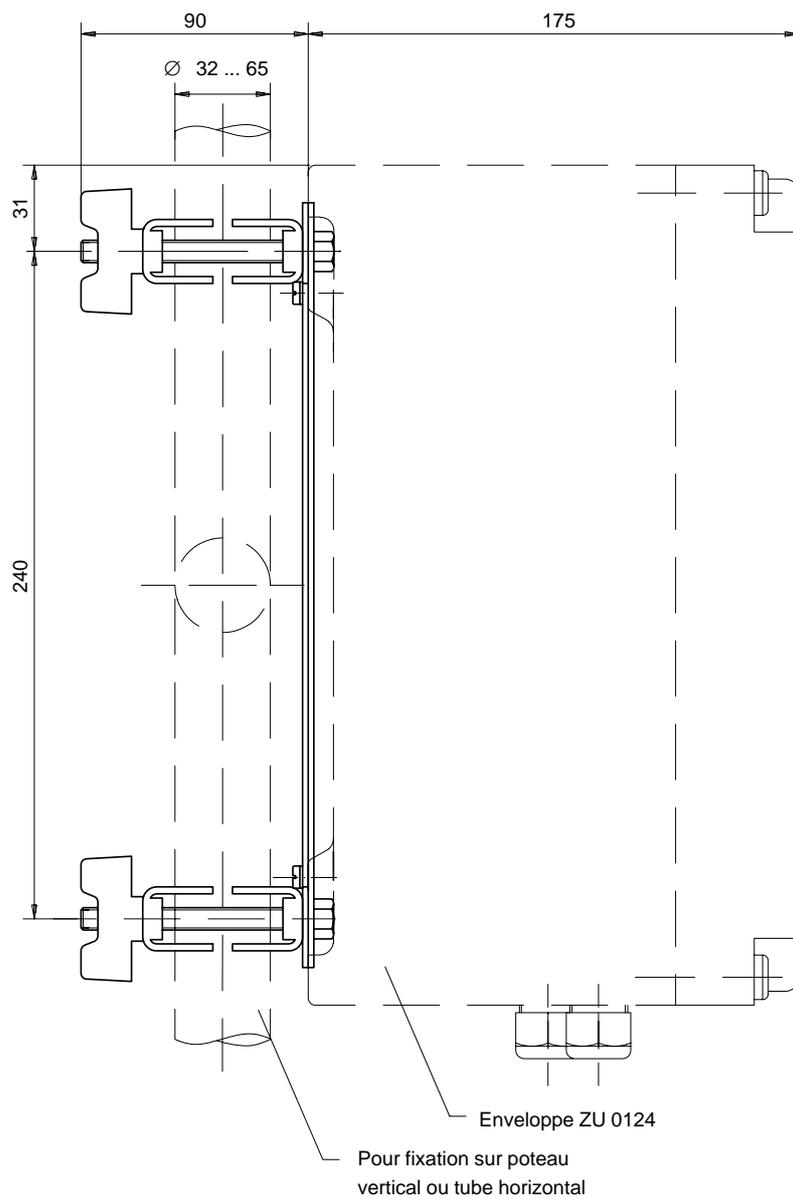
Boîtier ZU 0128 avec jeu de colliers de fixation sur poteau ZU 0124
